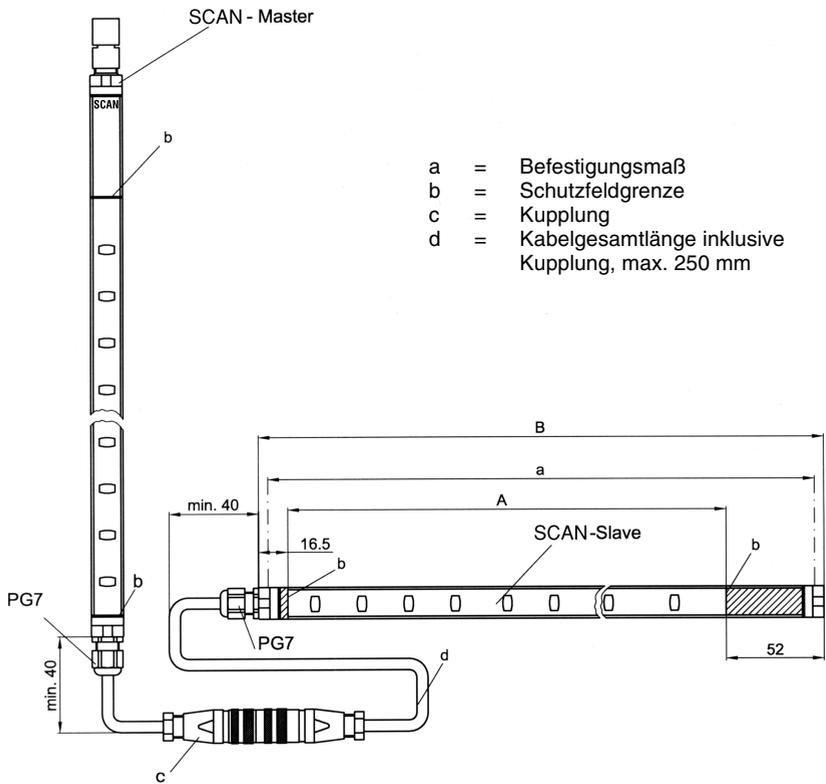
Maßzeichnung SCAN „kaskadierte Ausführung“
